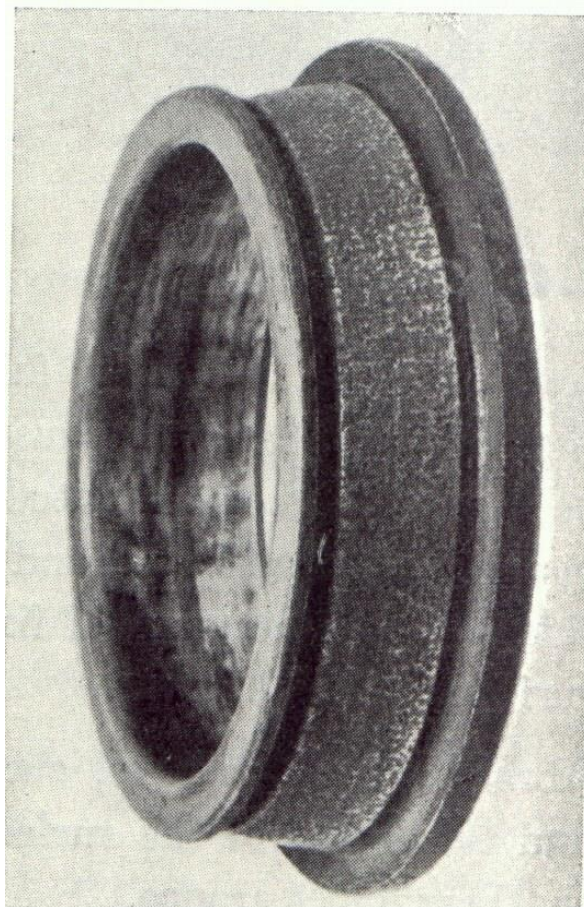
Daño por corrosión en pista interna de rodamiento cónico [2]
